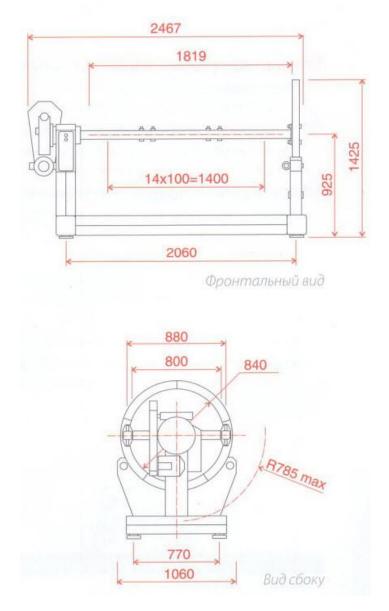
Стенд Р-776Е (габаритные размеры)
